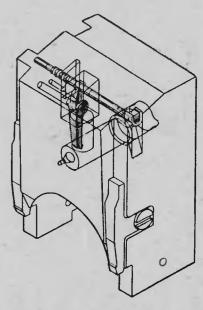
Детали ударного и предохранительного механизмов при сборке (вторая операция)
